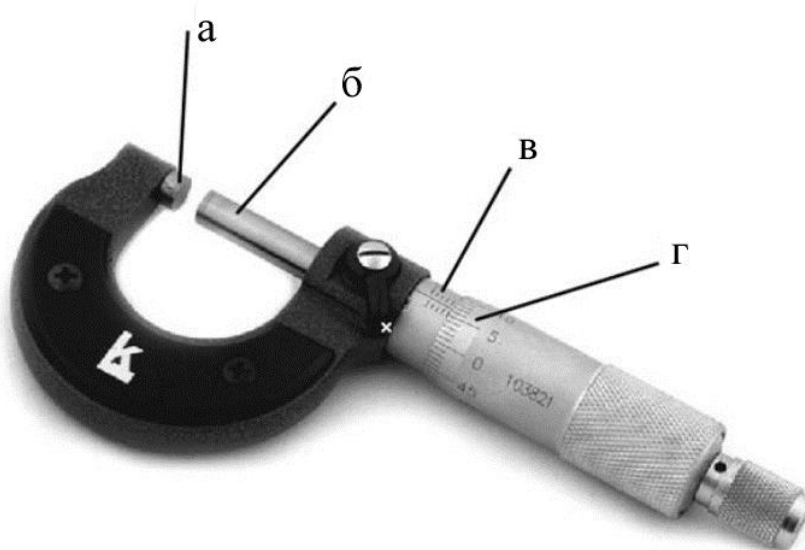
Устройство микрометра: а) неподвижный выступ; б) выступ микрометрического винта; в) линейная шкала; г) круговая шкала.
